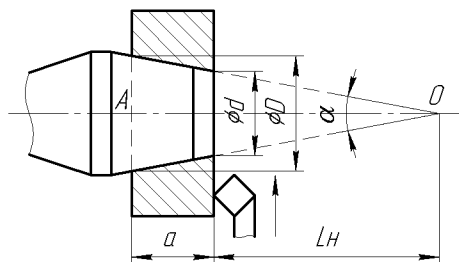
Визначення похибки базування при базуванні заготовки по конічному отвору
